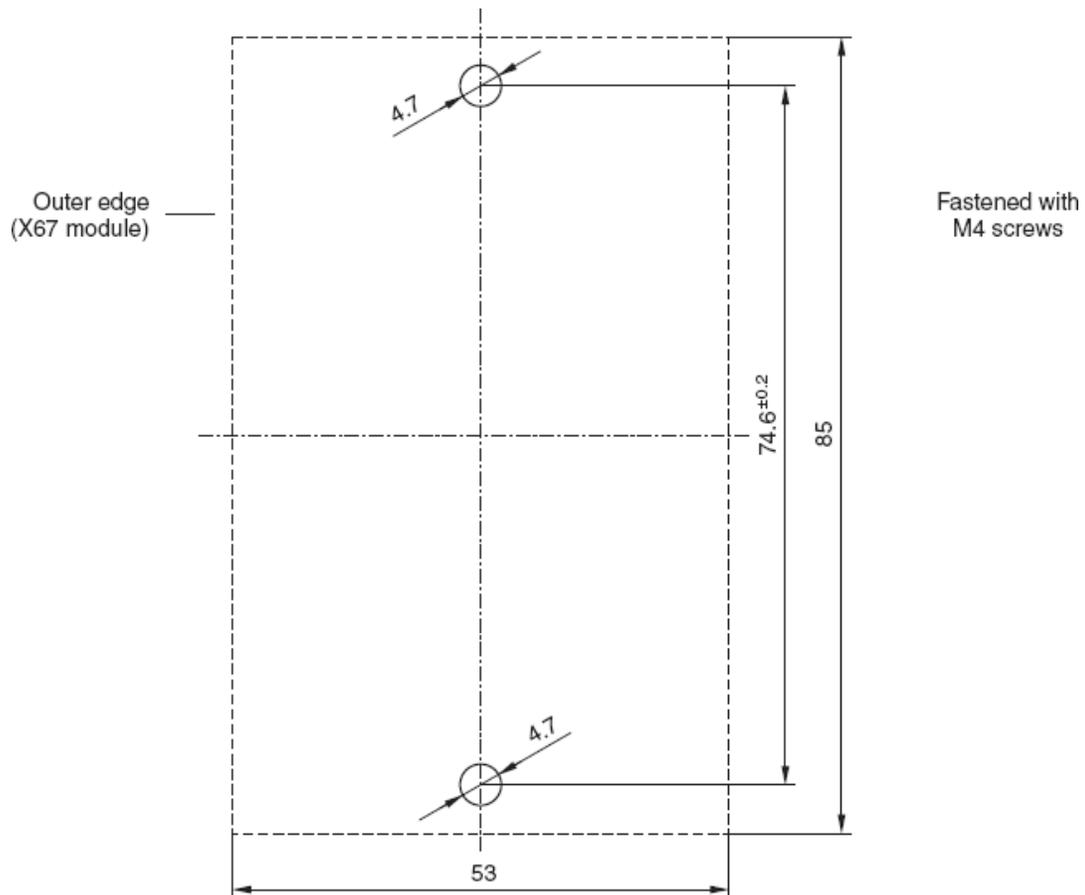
B. Bohrschablone für Schraubensbefestigung.
